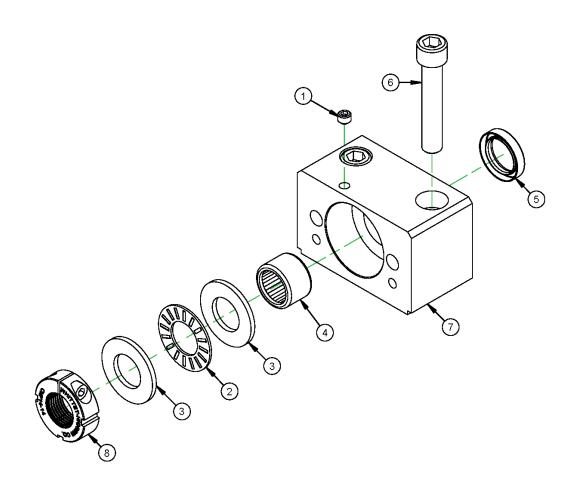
Kugelgewindetrieb-Baugruppe (P/N 66472)
